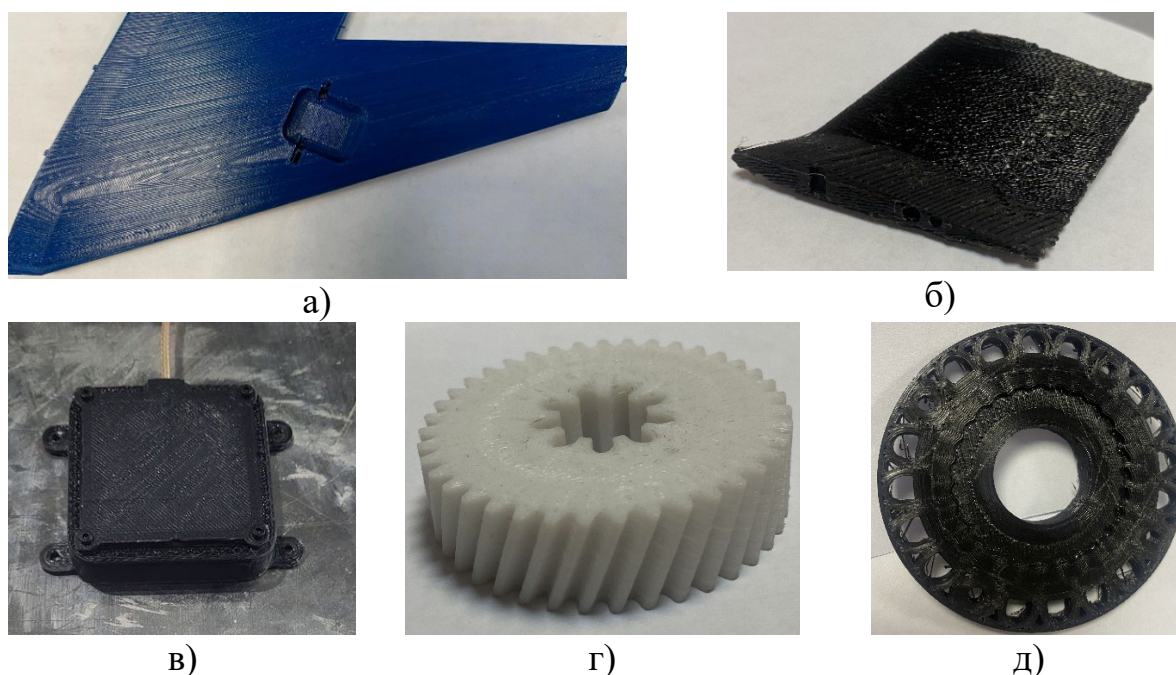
Примеры обрабатываемых деталей: а – фрагмент крыла БПЛА, из материала PETG; б – вертикальная законцовка крыла, из материала TOTAL GF-15; в – корпус датчика БПЛА, из материала PETG; г- шестерня редуктора, из материала PETG; д – корпус волнового редуктора, из материала TOTAL GF-15.
